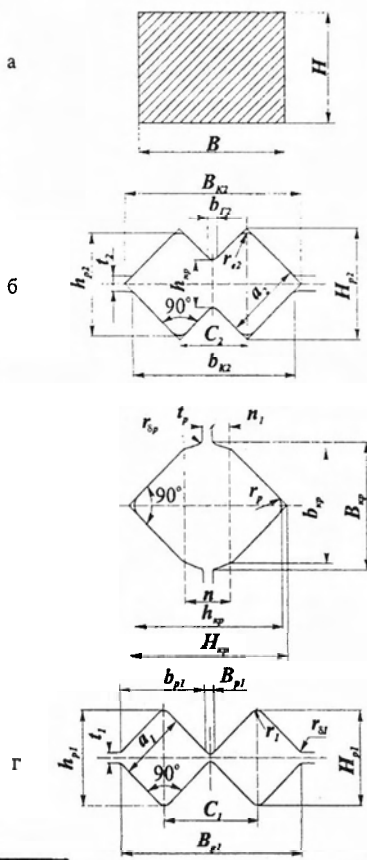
Схема калибровки валков для двухручьевой прокатки-разделения квадратных профилей с продольным разделением раската контролируемым разрывом: поперечные сечения: а - заготовки; б - г - калибров
